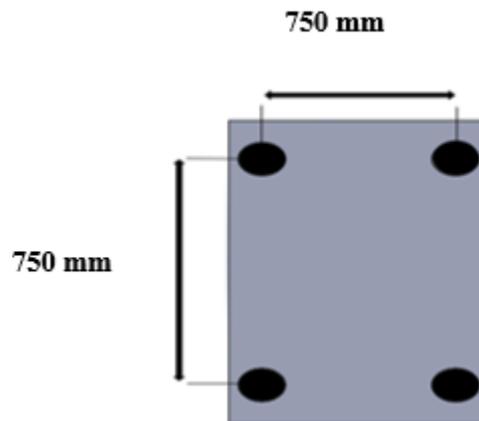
Schémas d'un plateau d'une presse 225 T [27]
